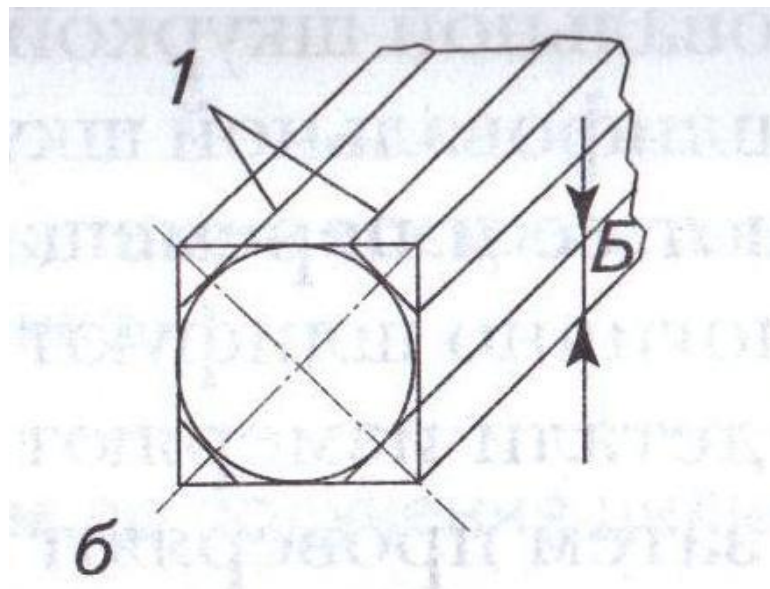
Последовательность изготовления детали цилиндрической формы ручным инструментом.
